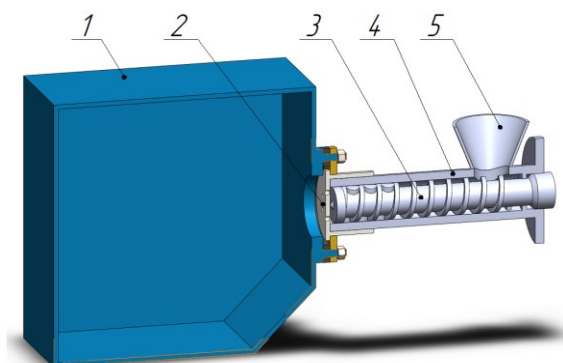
Схема одношнекового экструдера с вакуумной камерой: 1 – вакуумная камера; 2 – матрица; 3 – шнек; 4 – корпус; 5 – горловина
